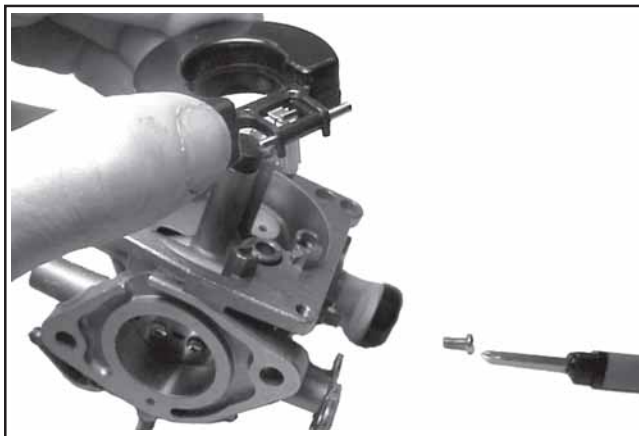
Rimozione di galleggiante e spillo di ingresso.
